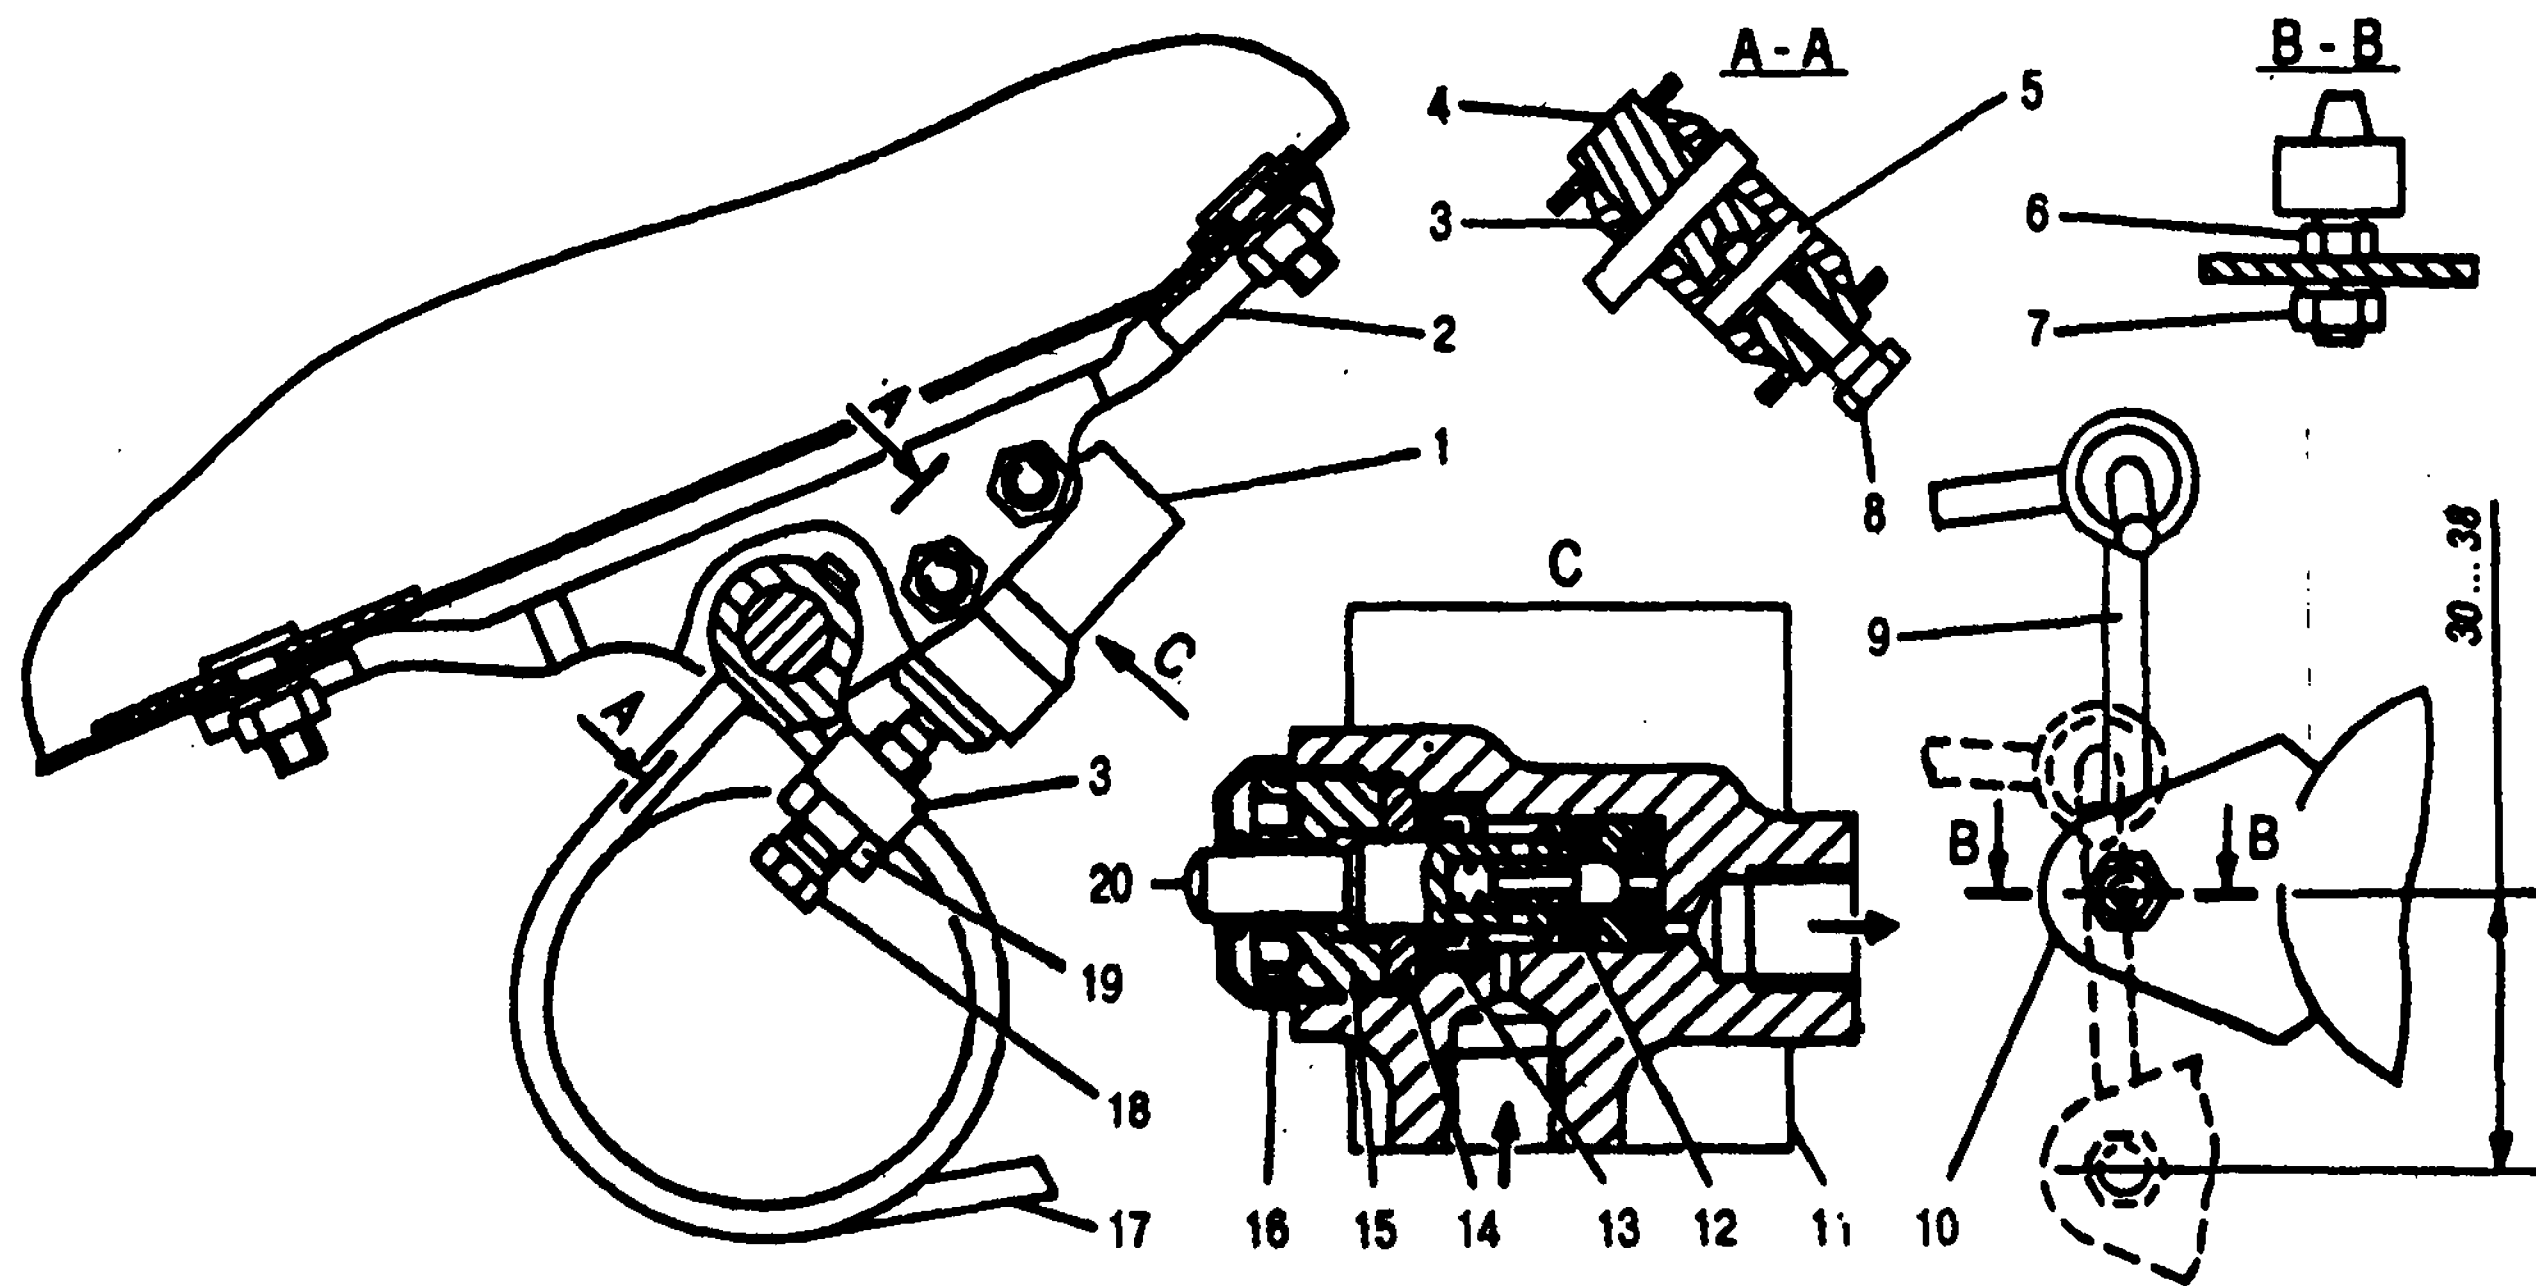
Регулятор давления задних тормозов: 1 - регулятор; 2 - переходный кронштейн; 3 - нажимной рычаг; 4 - ось нажимного рычага; 5 - штифт; 6 - ось; 7 - гайка; 8 - фиксирующий болт; 9 - стойка регулятора; 10 - кронштейн стойки; 11 - корпус регулятора; 12 - манжета большой ступени поршня; 13 - манжета малой ступени поршня; 14 - втулка; 15 - пробка; 16 - чехол; 17 - упругий элемент; 18 - регулировочный болт; 19 - контргайка; 20 - поршень в сборе
